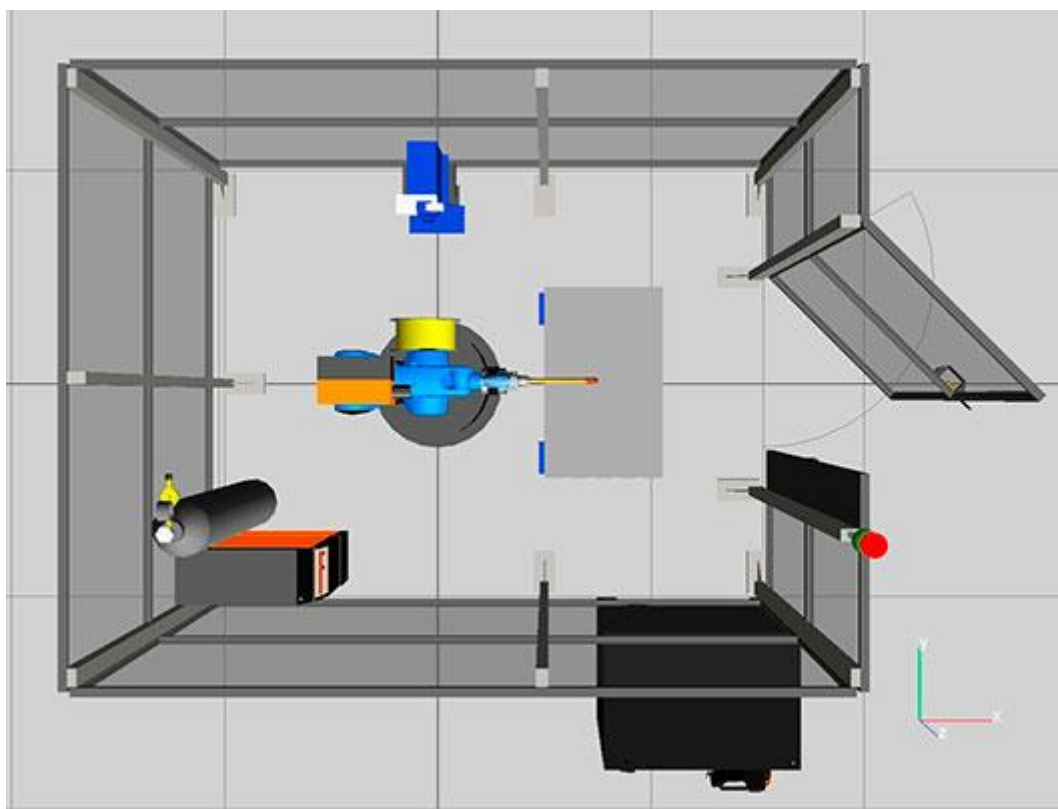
Сварочный робот KUKA / Сварочная машина Fronius.
